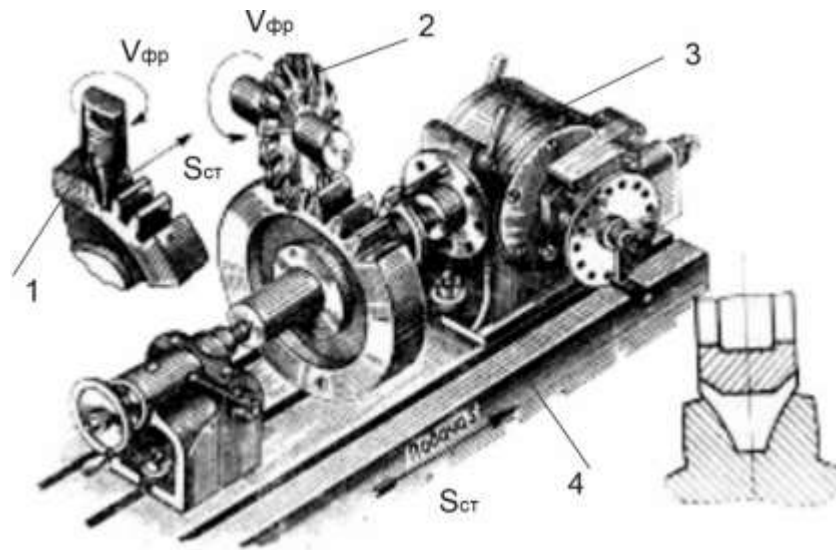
Схема обробки циліндричних зубчастих коліс методом копіювання:
